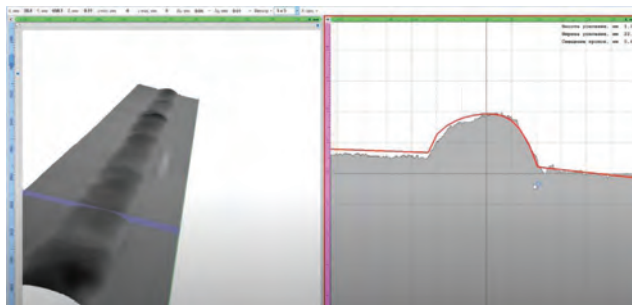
Построение профиля сварного шва лазерным триангуляционным датчиком
